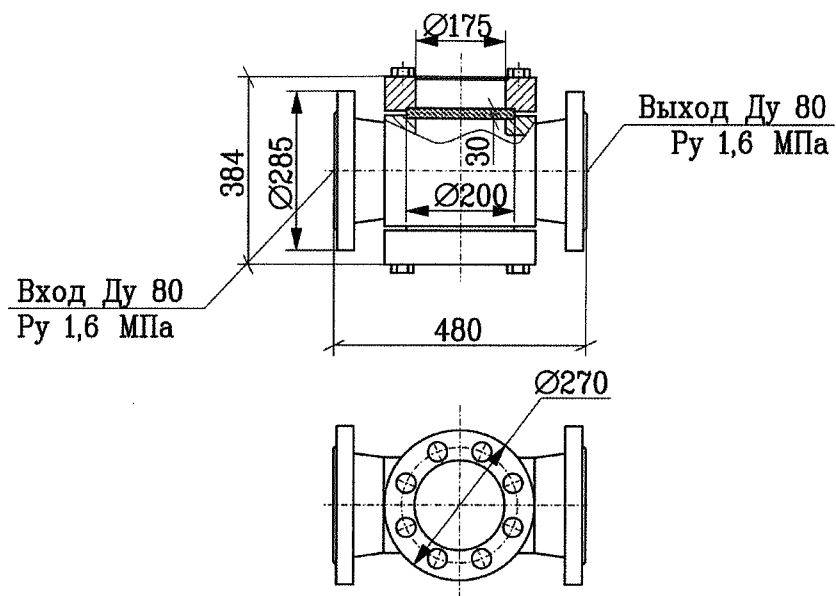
Габаритный чертеж фонаря смотрового LDP41AX001, LDP43AX001
